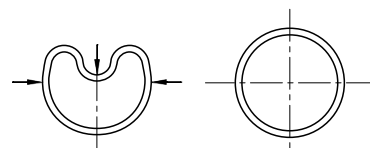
Slipper Seal®, уплотнение штока, установка 2
